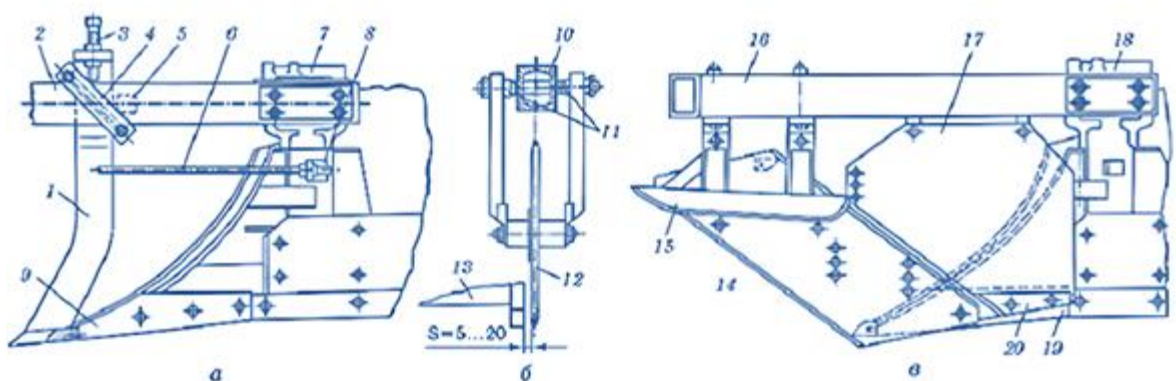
Робочі органи чагарниково- болотних плугів: а – череслового (ПБН- 75); б – дискового (ПБН- 75); в – плоского з опорною лижею (ПБН- 100А); 1 – чересловий ніж; 2 – рама; 3 – болт; 4 – плита; 5 – рама; 6 – натяжний прутко; 7 – стояк корпусу; 8 – кронштейн; 9 – планка лемеша; 10 – рама плуга; 11 – регулювальні шайби; 12 – дисковий ніж; 13 – долото; 14 – плоский ніж; 15 – опорна лижа; 16 – рама; 17 – щиток; 18 – корпус; 19 і 20 – планки
